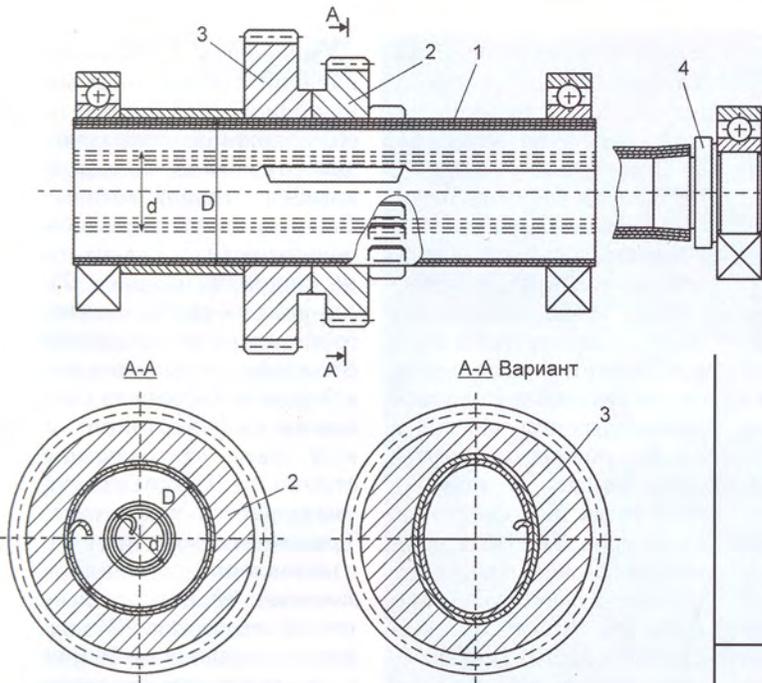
Навитой из ленты вал передачи в сборе с деталями:
